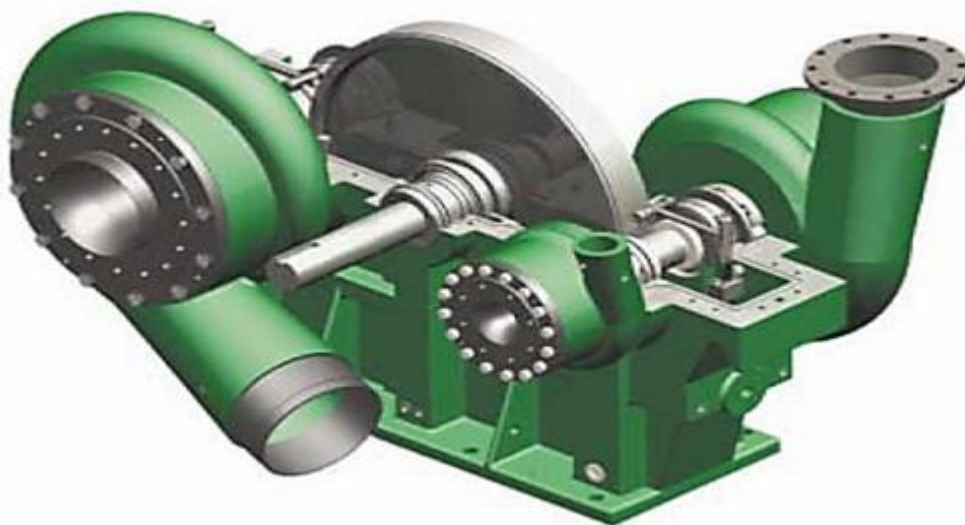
Центробежный газовый компрессор с горизонтальной линией разъема
